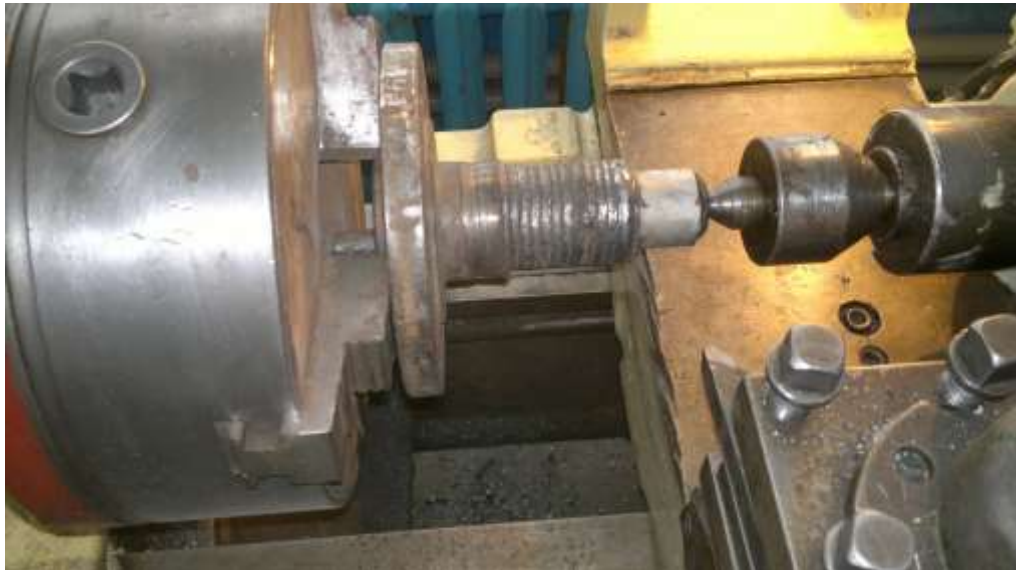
Наплавлений вал підготовлений для проточування
